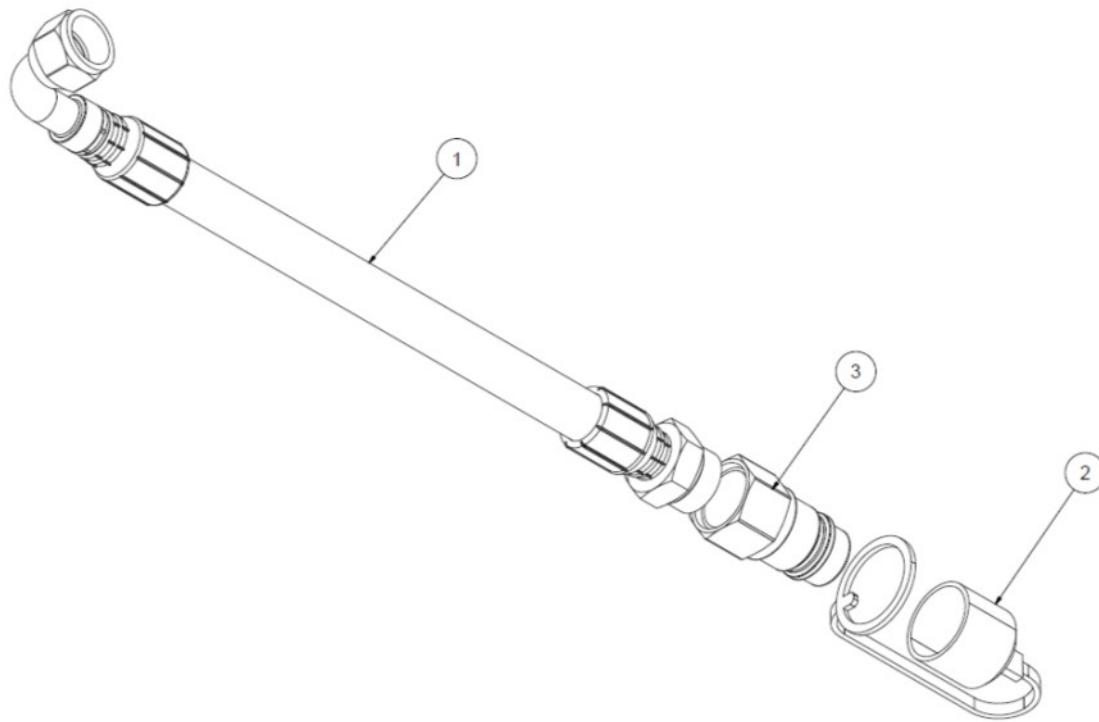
Чертеж сборки шланга гидравлического цилиндра опрокидывания кузова - растягивание – 815614
